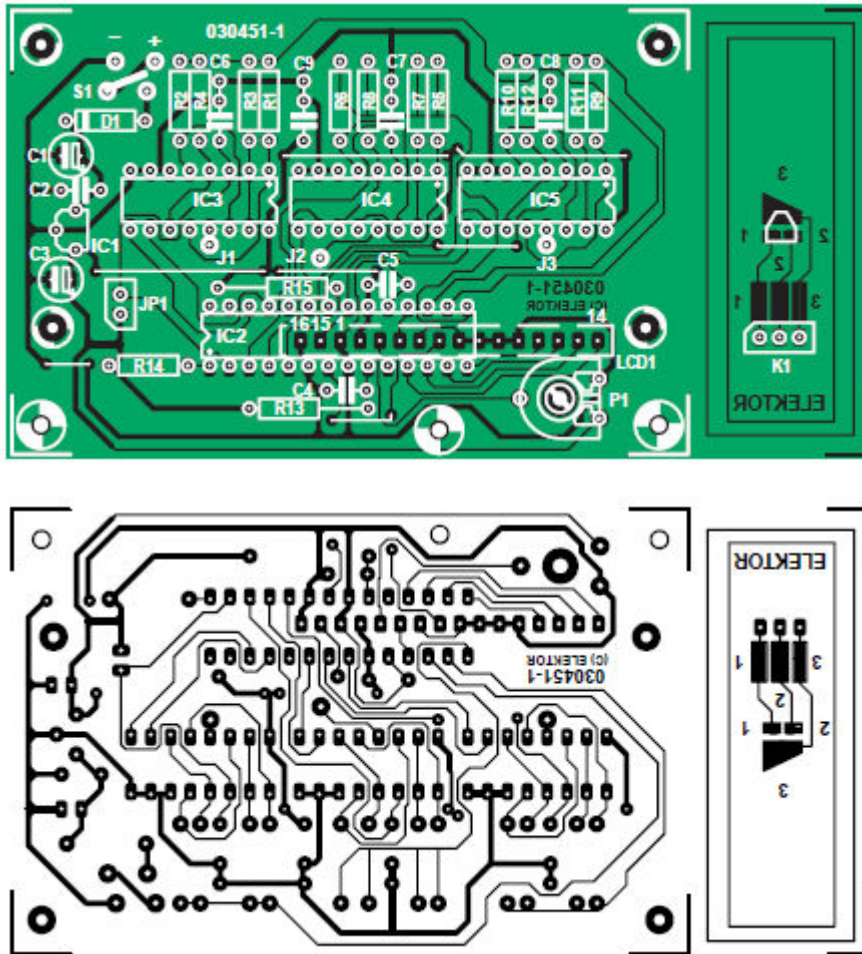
layout* das trilhas e disposição dos componentes da placa PCB
